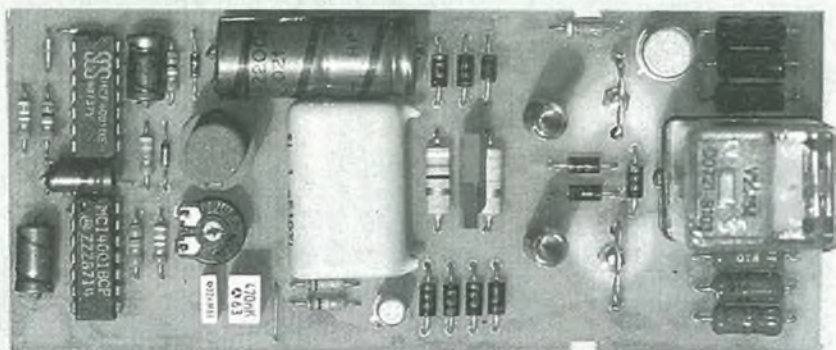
Vista del fusibile elettronico a montaggio ultimato.
